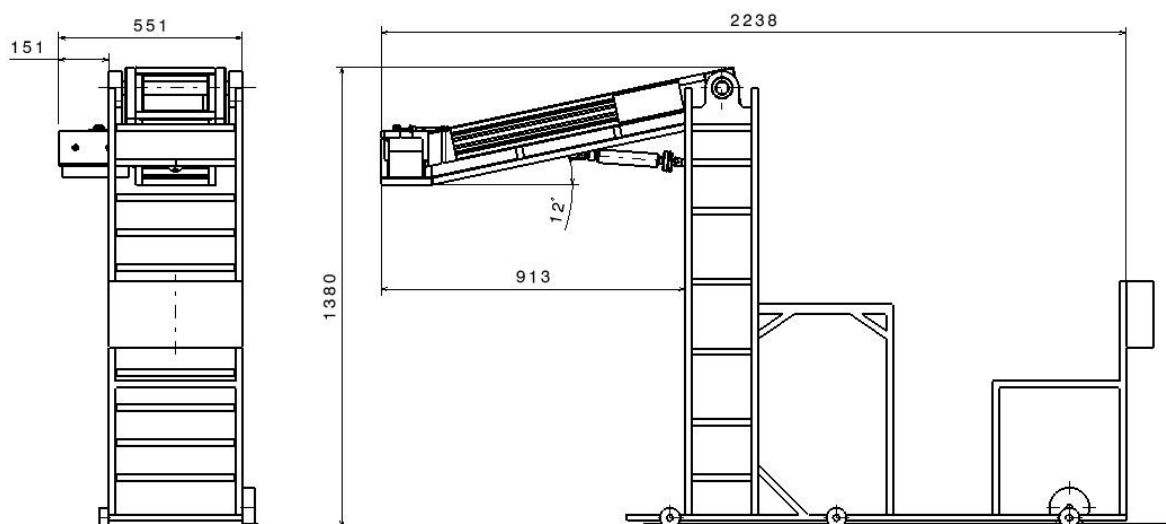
Alimentador de matéria-prima para um centro de usinagem três eixos
